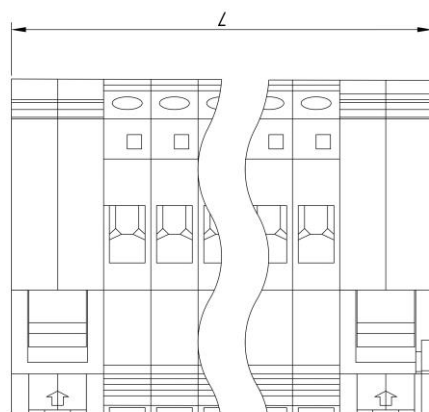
Общий вид базового блока ЭПББ. Вид сверху.
